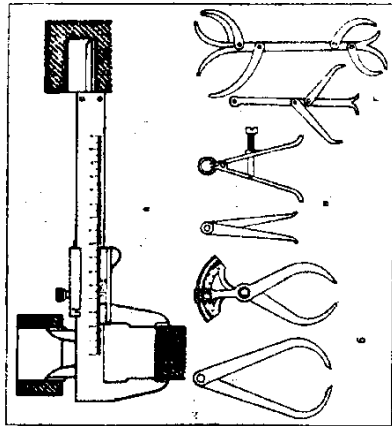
Контрольно-измерительный инструмент: а — штангенциркуль; б — кронциркуль; в — нутромер; г — комбинированный измерительный инструмент
